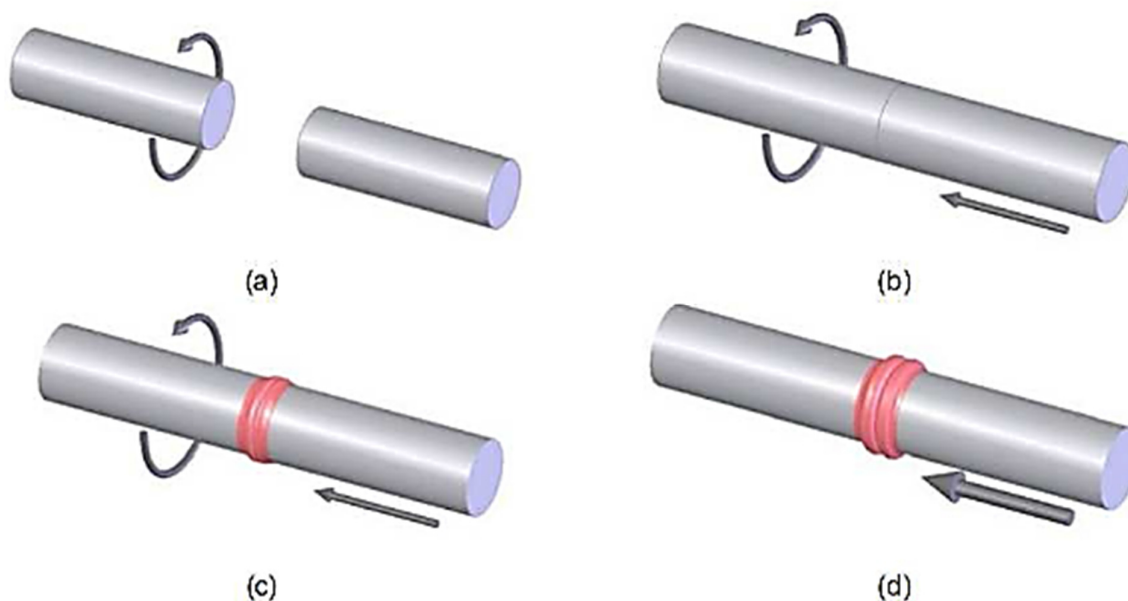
Desenho esquemático do processo de soldagem por atrito convencional (*Direct Drive* ou *Continuous Drive*) (AWS 1991 e PINHEIRO 2008): a) Rotação de uma das peças; b) Aplicação da Força de Compressão; c) Início da soldagem; d) Fim da soldagem.
